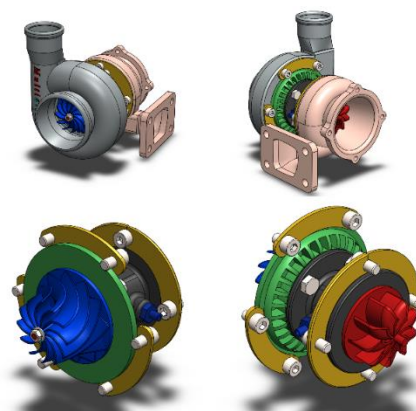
Modelo 3D del turbocompresor, derecha turbo, izquierda compresora
